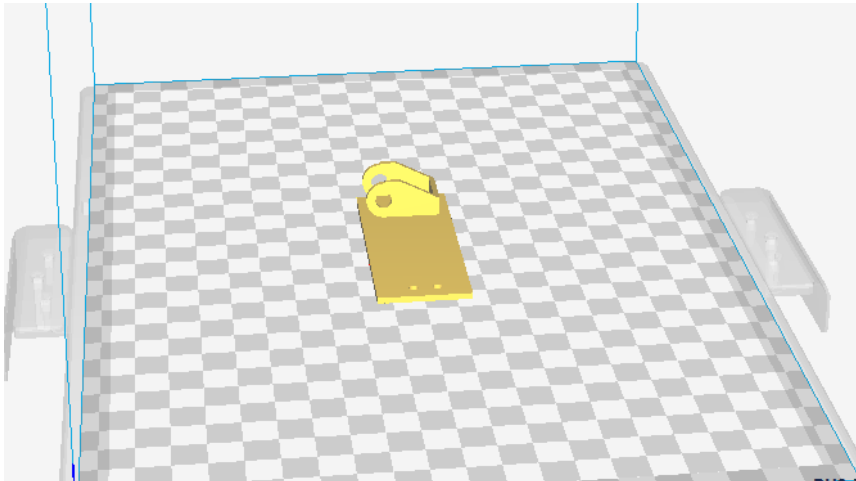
Posición de impresión del acoplador 1 de cadena.
